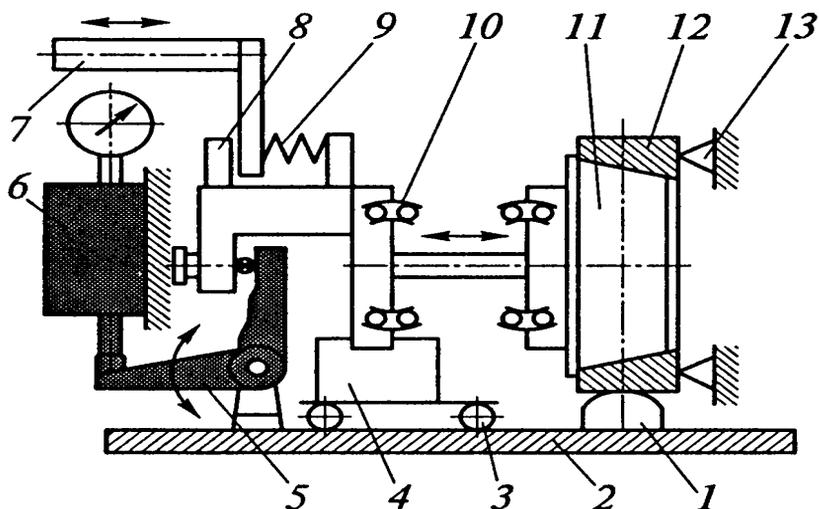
Блокировочное устройство для контроля величины припуска в отверстии: 1 – призма; 2 – плита; 3 – направляющая; 4 – каретка; 5 – рычаг; 6 – электроконтактный преобразователь; 7 – толкатель; 8 – упор; 9 – пружина; 10 – шарнир; 11 – калибр-пробка; 12 – заготовка; 13 – опора
